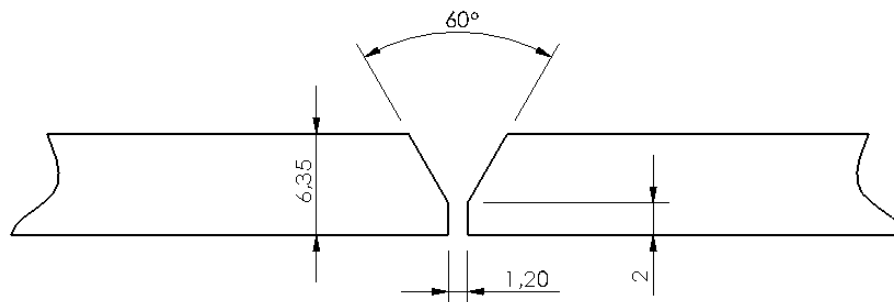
Dimensões do chanfro para soldagem MIG.
